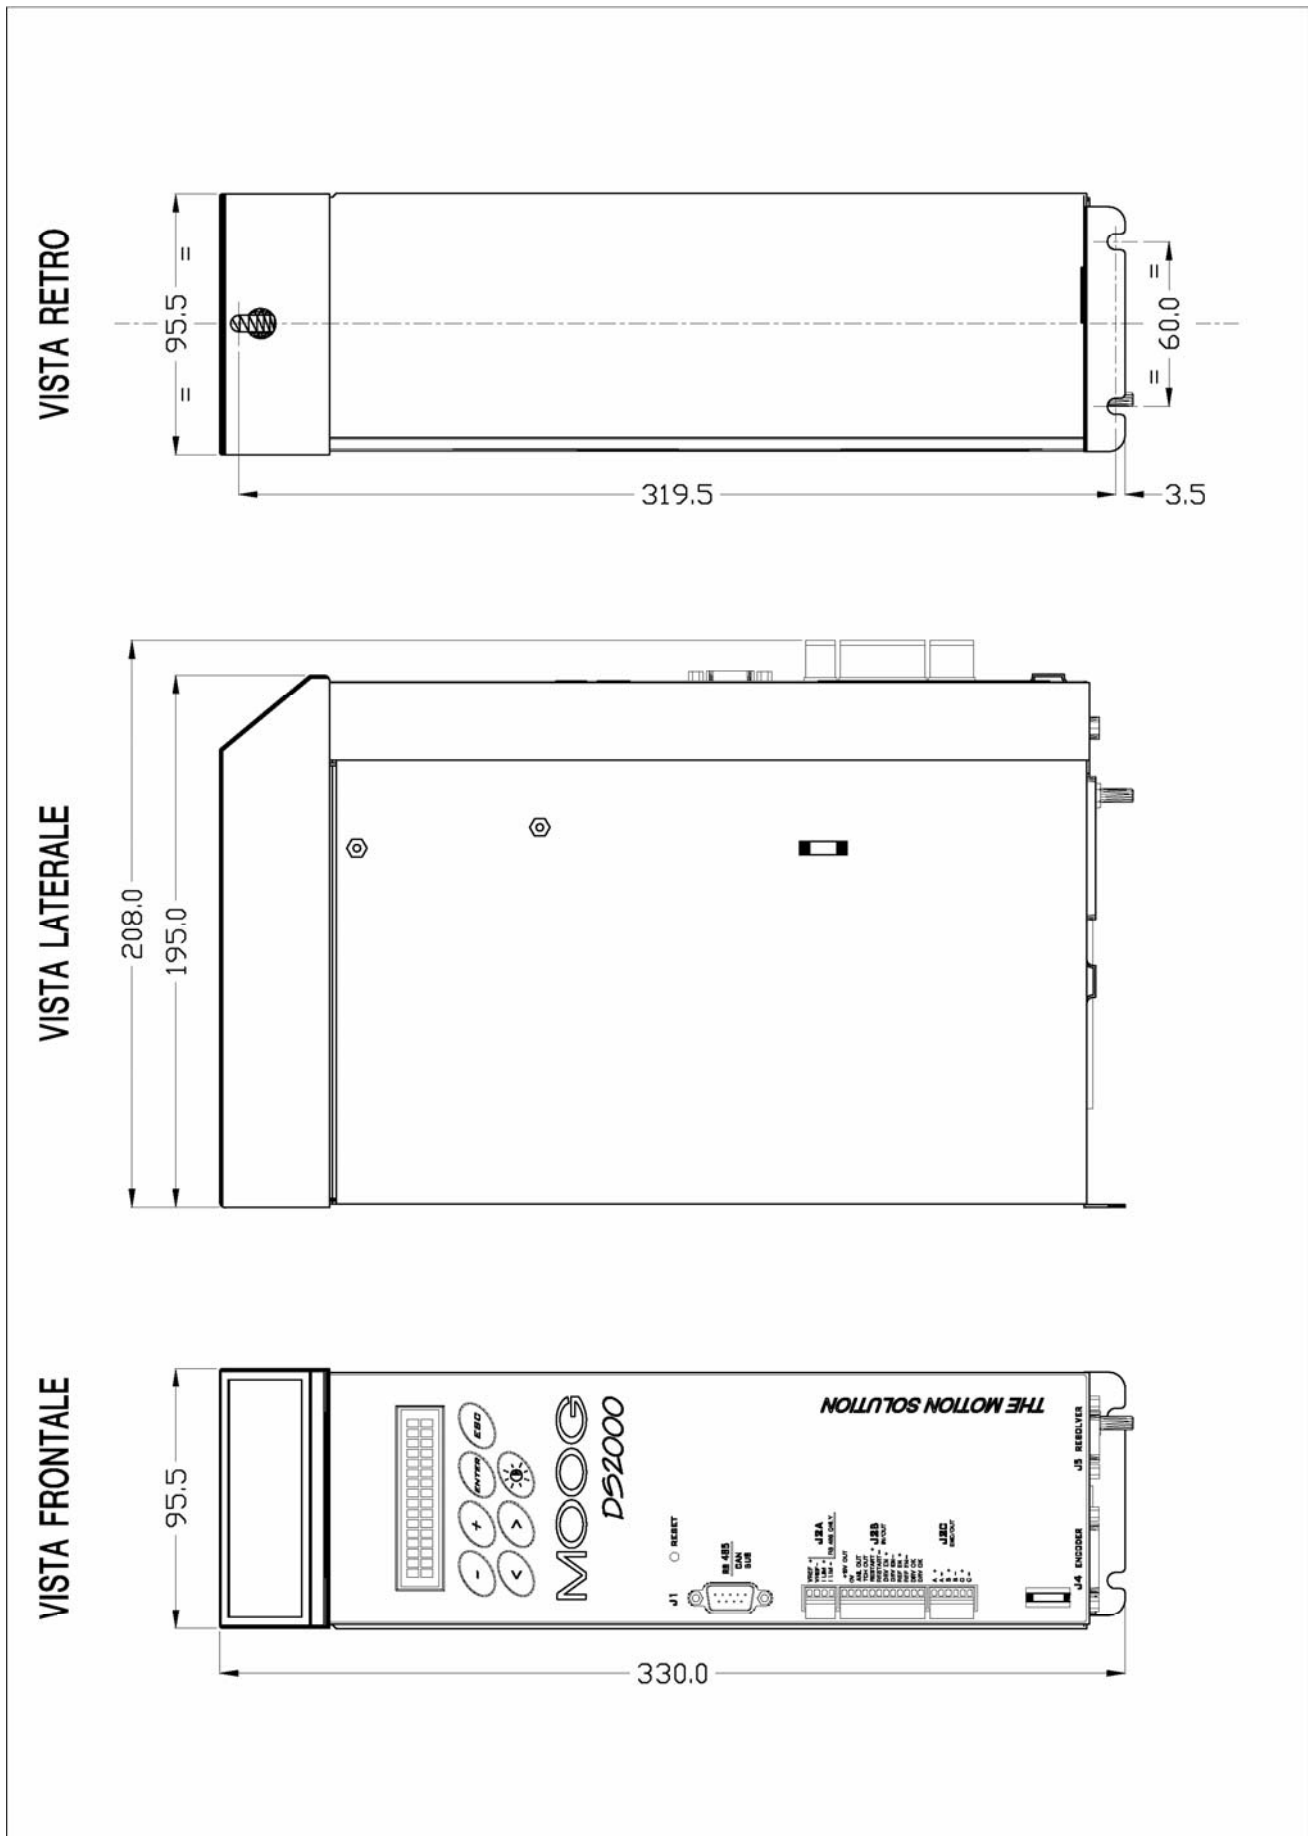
Dimensioni e fissaggi (mm) taglia A
